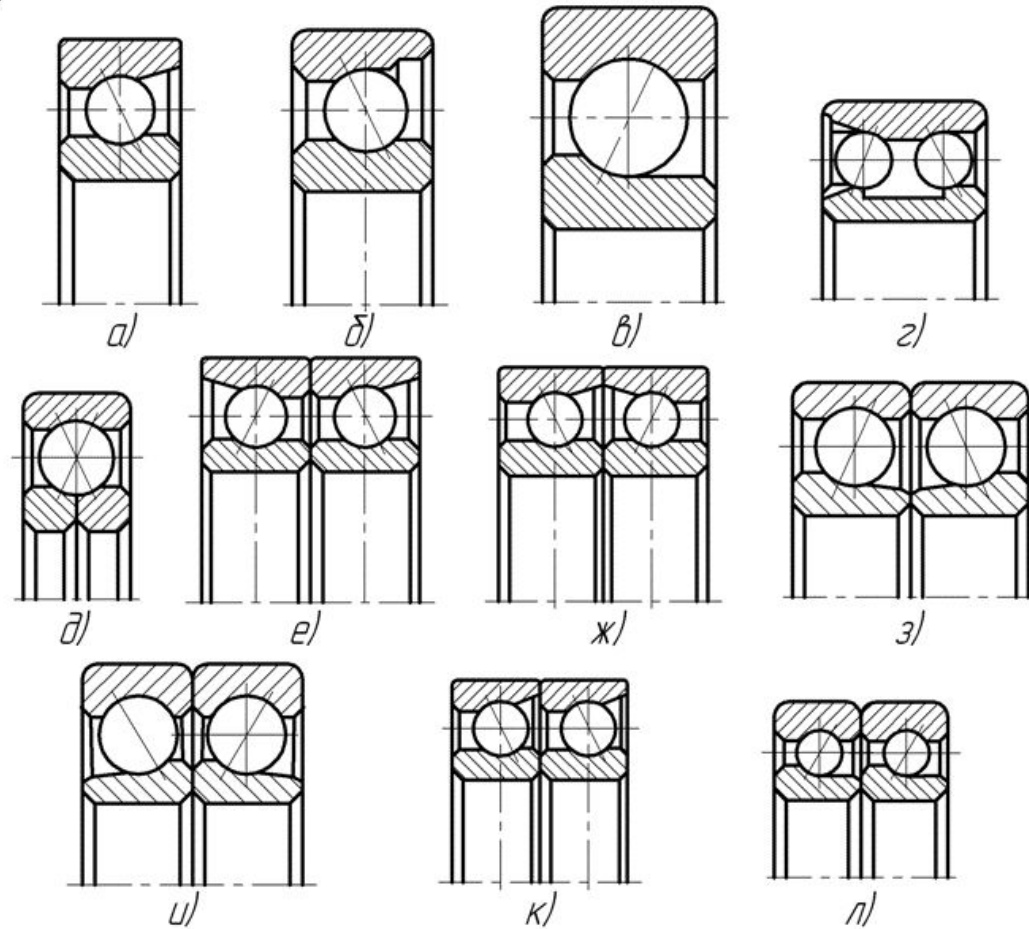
Подшипники радиально-упорные шариковые исполнений:
